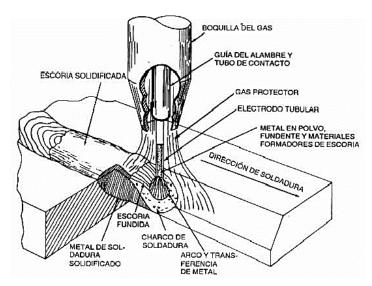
Esquema del proceso de soldadura FCAW-G
